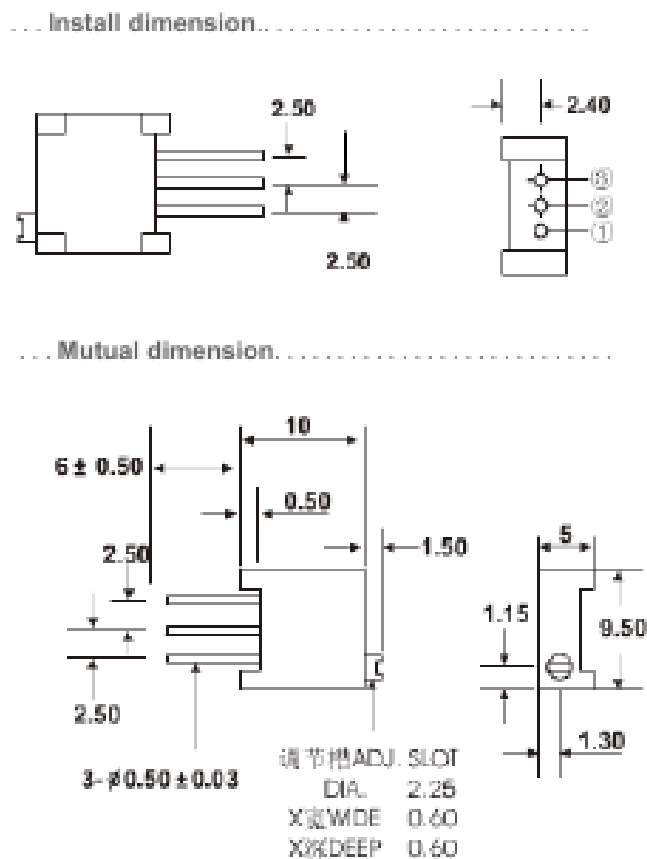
Габаритні розміри резистор підстроювальний 3296W-500K
